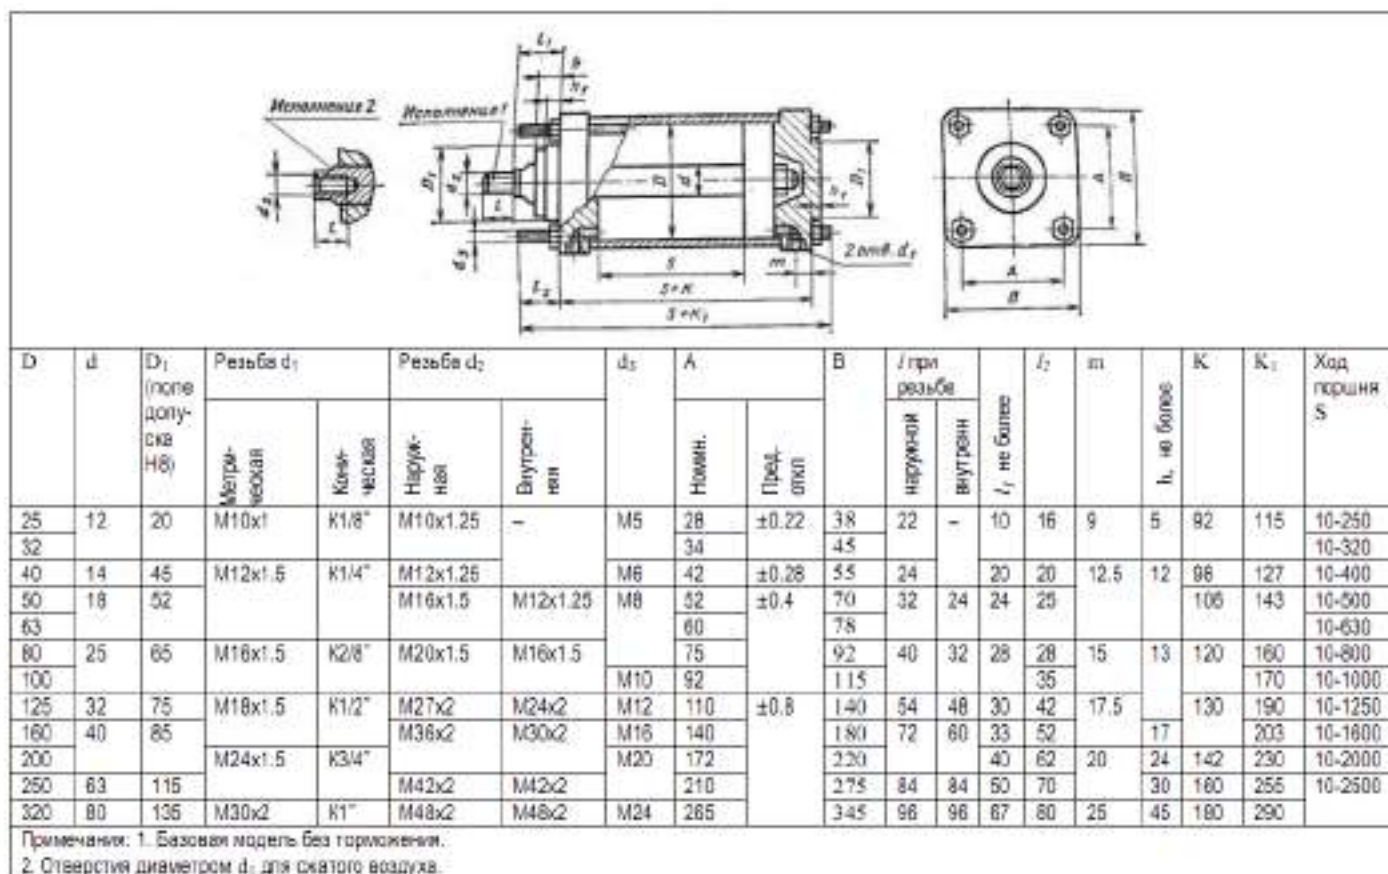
Пневмоцилиндры без торможения, размеры
